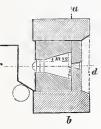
Grundriß nach gh. Einfacher Schachtofen.
